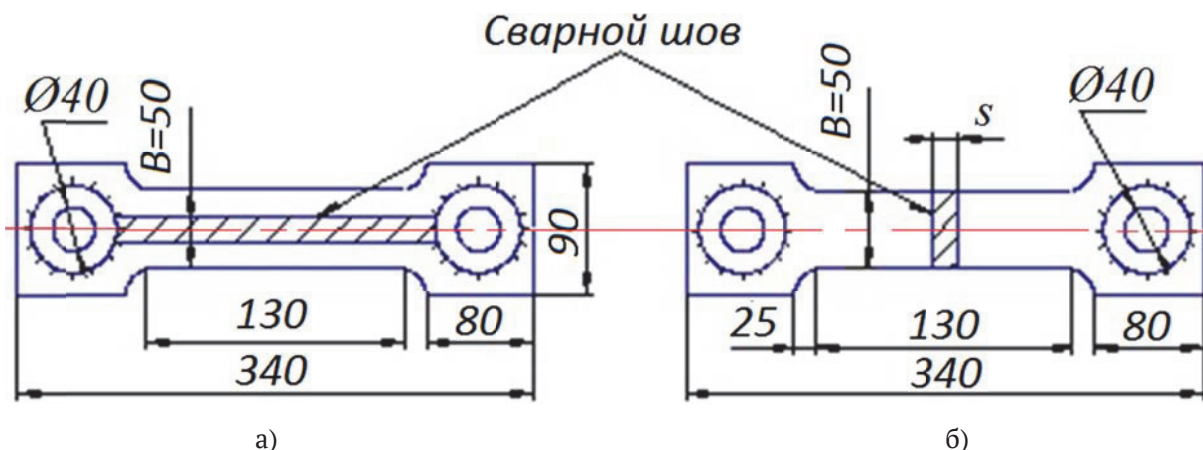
Широкие плоские образцы для исследования несущей способности сварных соединений стали 15X5M на одноосное растяжение
